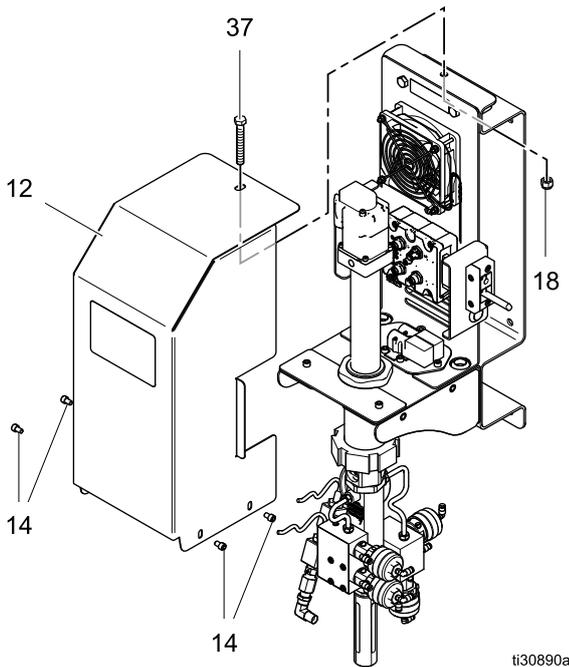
Instale la cubierta del kit de expansión (montaje en pared)
